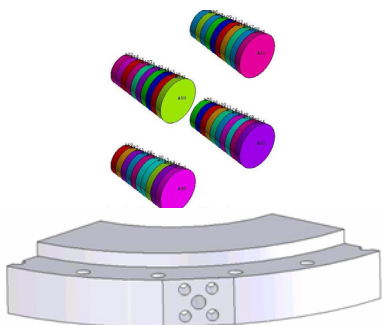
Геометрическая модель сварных швов и четверти фланца
